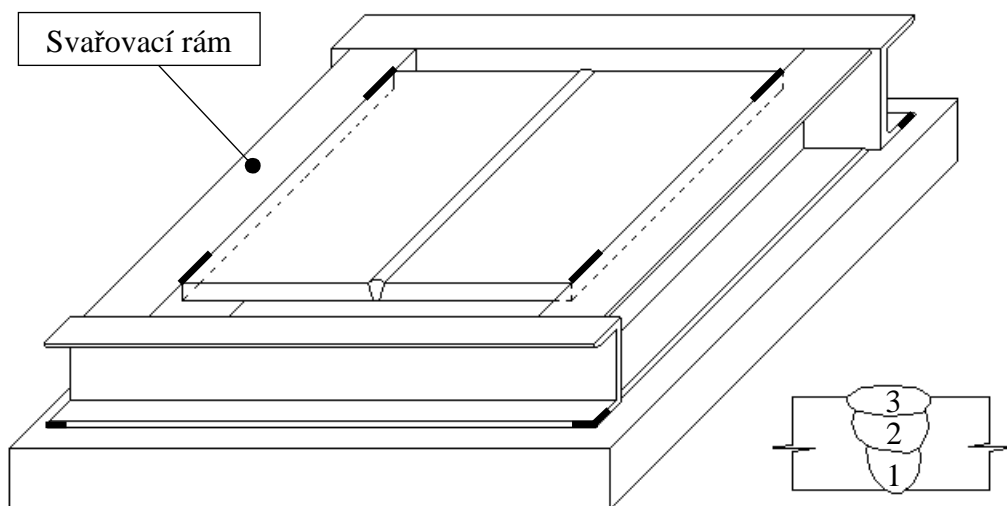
Znárodnění případu svařování T-svaru
